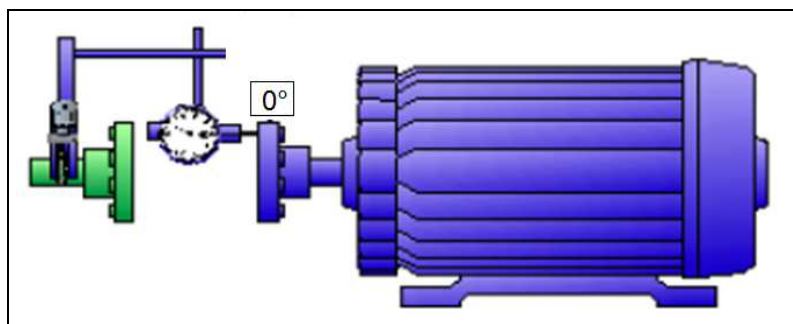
Posición inicial de medición FACE. Vista lateral de motor.
